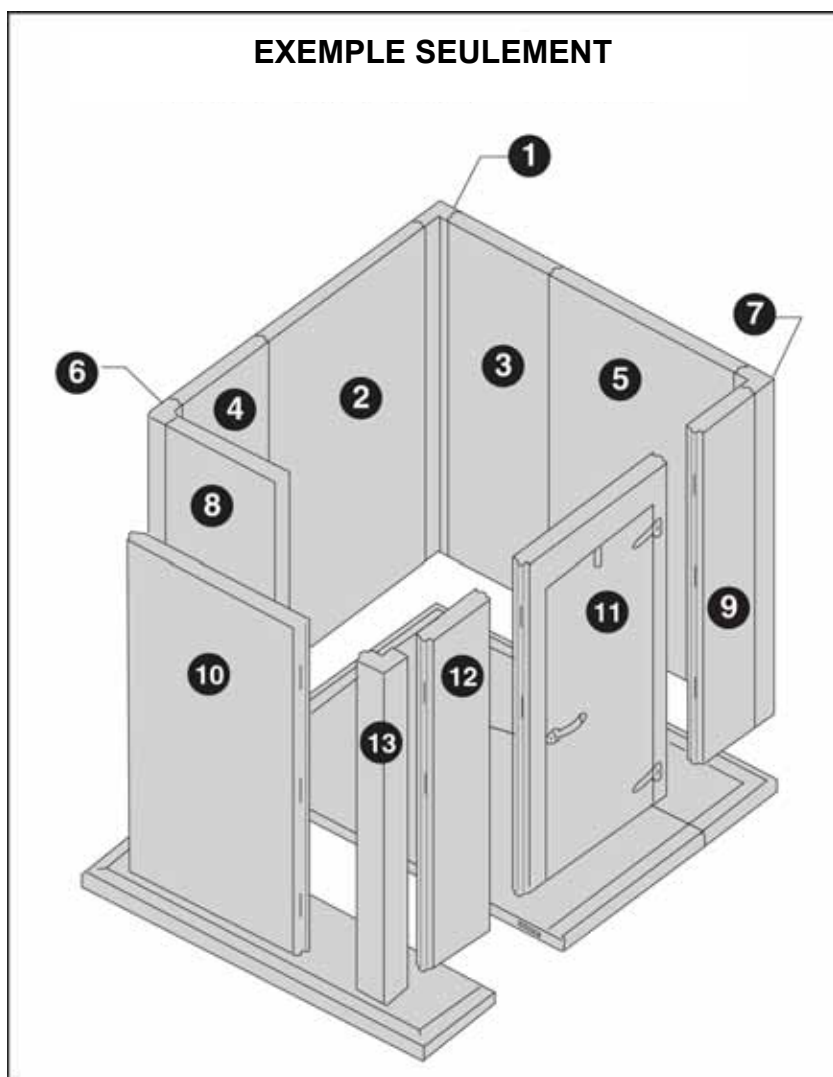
JOINTS DES PANNEAUX DE CONGÉLATEUR
